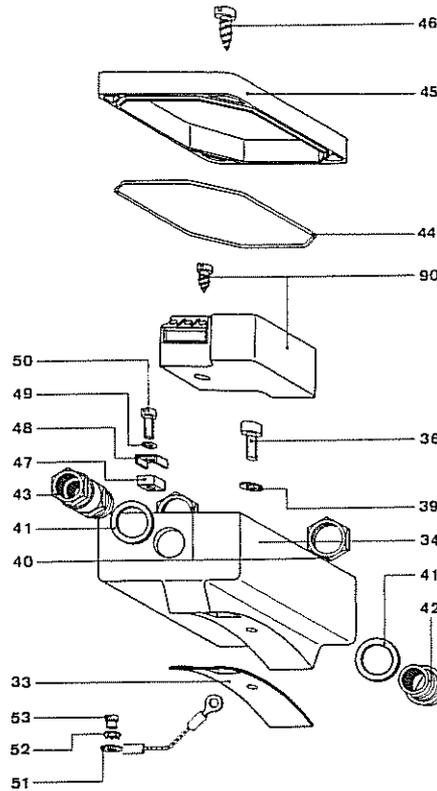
Anschlußgehäuse mit Siliziumgleichrichter
